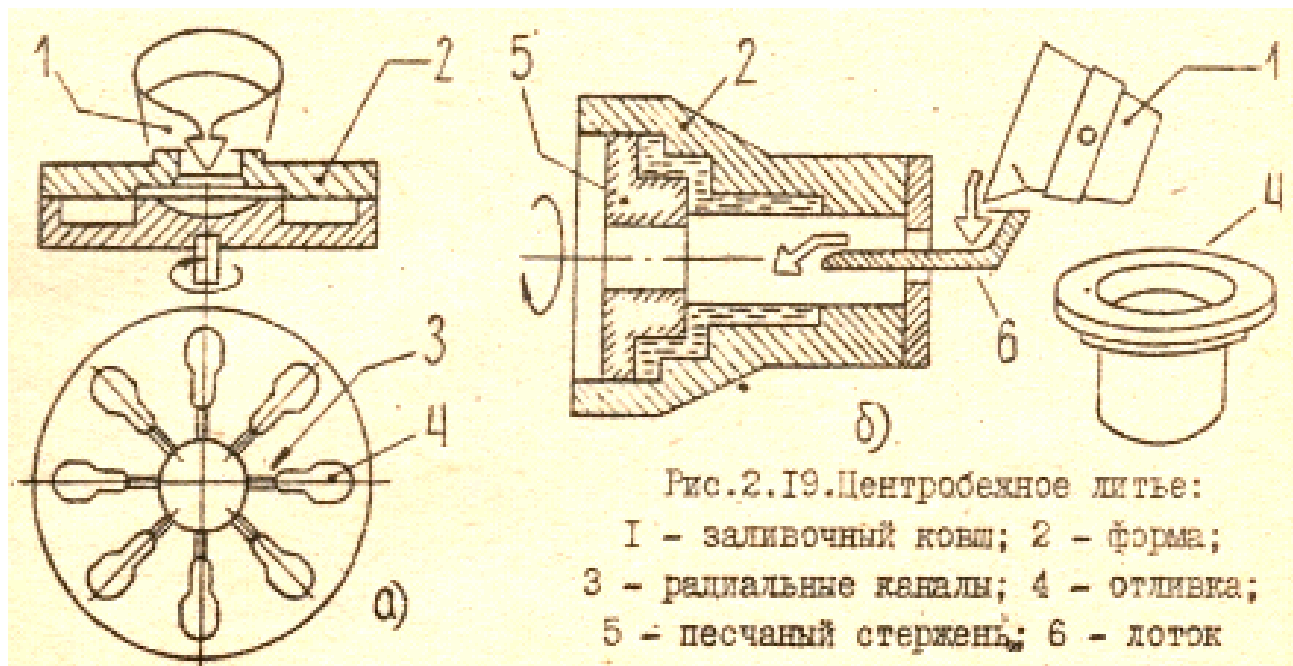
Центробежное литье: 1 — заливочный ковш;
